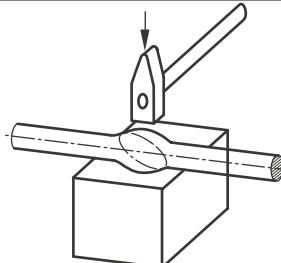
Wirkpaarungen beim Schweißen
